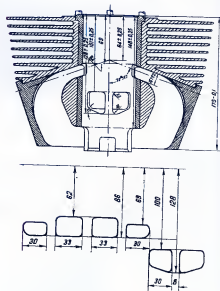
Цилиндр двигателя ИЖ-57 и его развертка (внизу).
